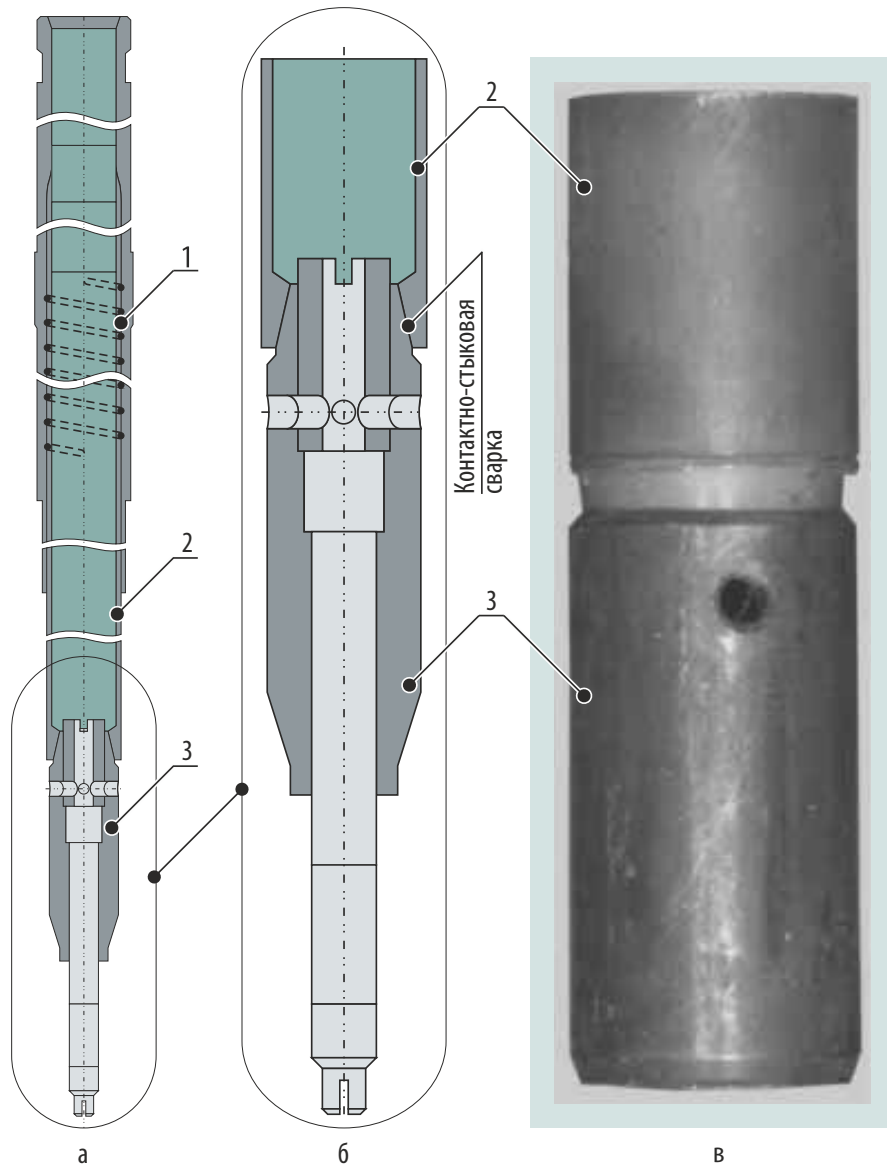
Схема направляющего канала (а, б): 1 — гильза; 2 — труба; 3 — наконечник и внешний вид образца (в) сварного соединения трубы направляющего канала и наконечника
